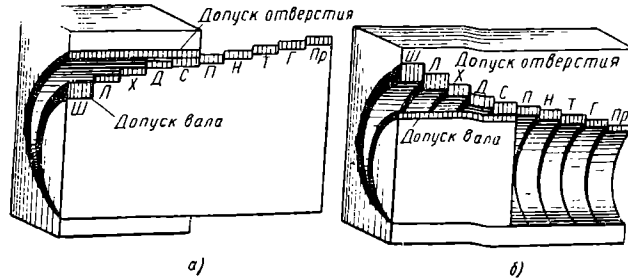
Схема расположения допусков при посадке с натягом.
